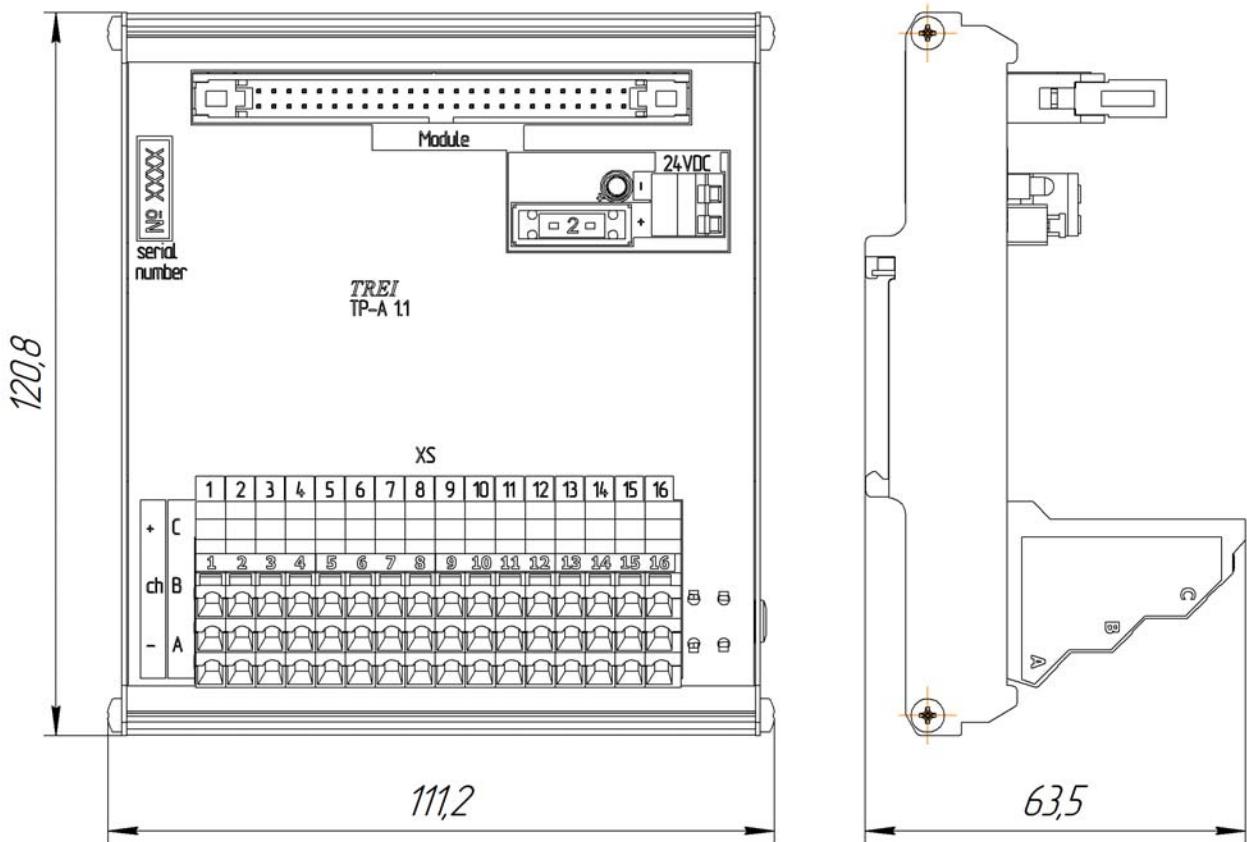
Чертеж общего вида ТР-А с указанием габаритных размеров
